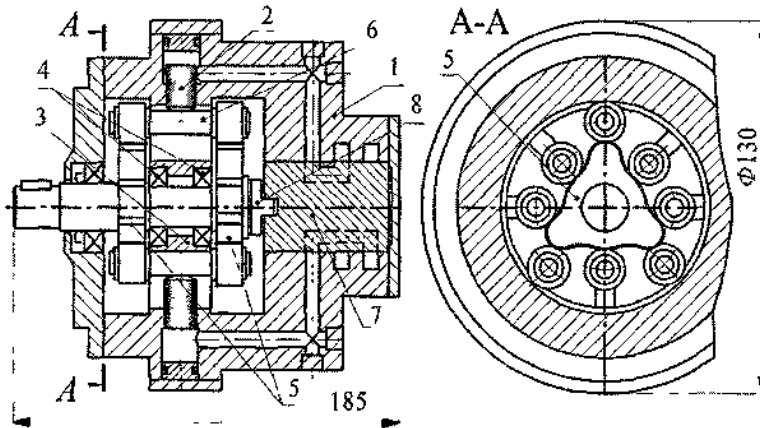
Миниатюрный радиально-поршневой гидромотор многократного действия типа МРФ-16/100 конструкции ВНИИГидропривода с разгрузкой поршней 2 с помощью траверс 6 в пазах статора 3 блока цилиндров 1
